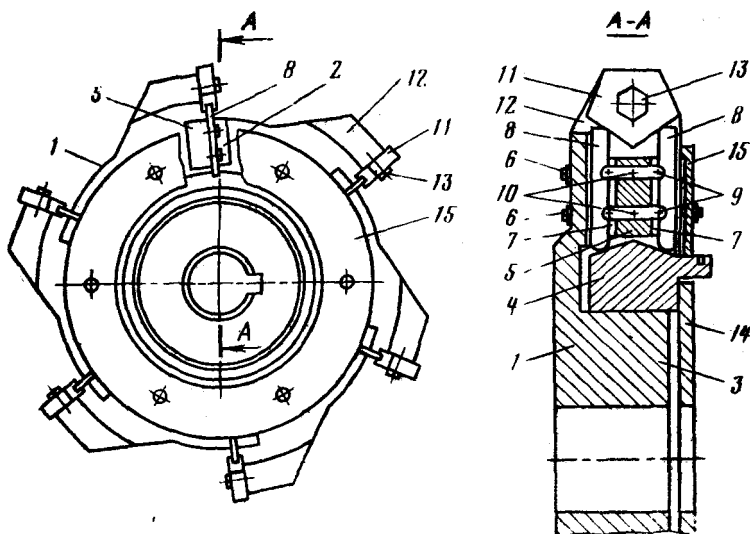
Дисковая фреза с твердосплавными многогранными пластинами для термофрезерования наплавленного металла при совмещенной комплексно-механизированной технологии восстановления детали: 1 — корпус; 2 — паз; 3 — ступица; 4 — обойма с круговым конусом; 5 — направляющая вставка; 6 — болт; 7 — радиальный паз; 8 — опорный элемент; 9 — шарнирно-рычажный механизм; 10 — винт-ось; 11 — твердосплавная многогранная пластина; 12 — зуб фрезы; 13 — болт-штифт; 14 — шайба; 15 — крышка
